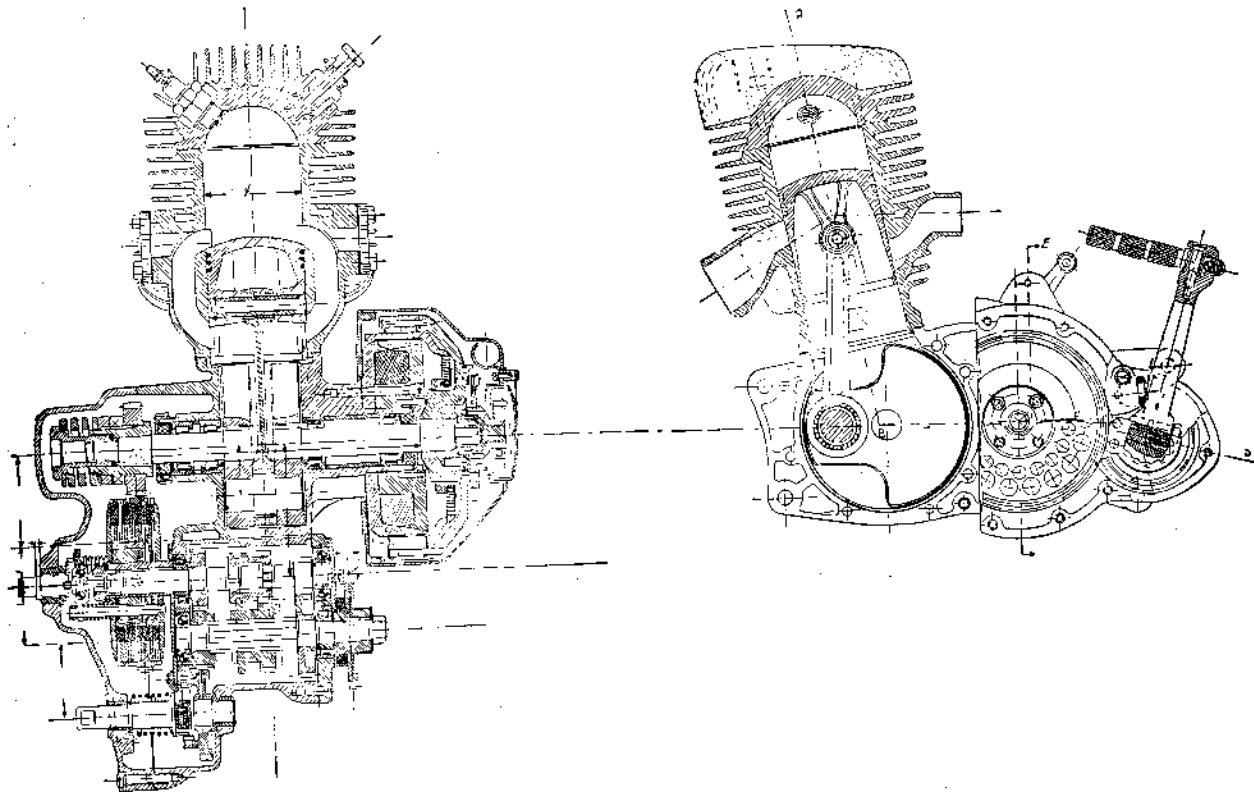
Schnitt und Draufsicht durch Motor-Getriebeblock des Typ SB 350.
